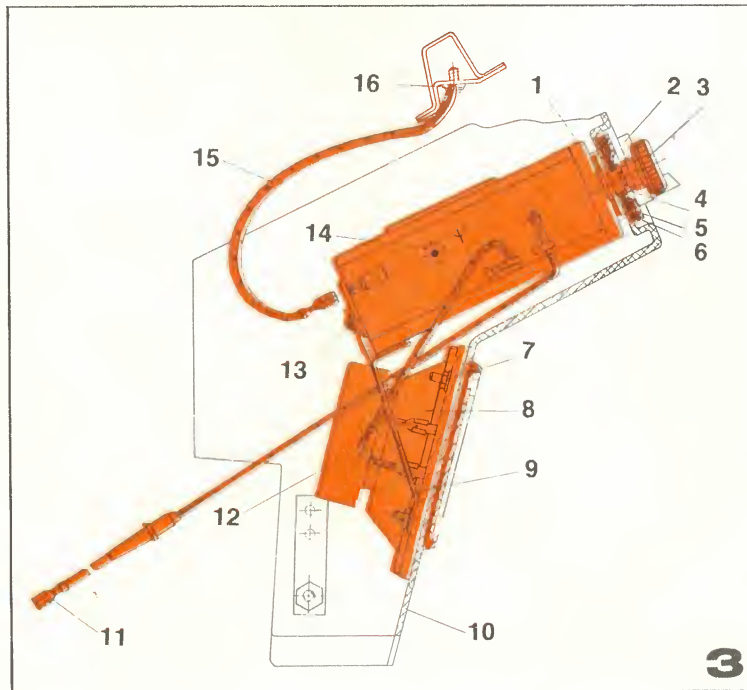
Установка приемника и динамика: 1 — радиоприемник А-271; 2 — рычаг; 3 — ручка; 4 — гайка; 5 — накладка; 6 — обрамление; 7 — гайка М5; 8 — громкоговоритель 4ГД-8Е; 9 — кронштейн крепления радиоприемника и громкоговорителя; 10 — панель; 11 — провод питания к клемме «INT»; 12 — экранированный провод; 13 — винт М5x8 крепления приемника; 14 — гнездо под штеккер антенны; 15 — провод «массы» приемника; 16 — зубчатая шайба диаметром 5 мм под винт «массы» приемника.
